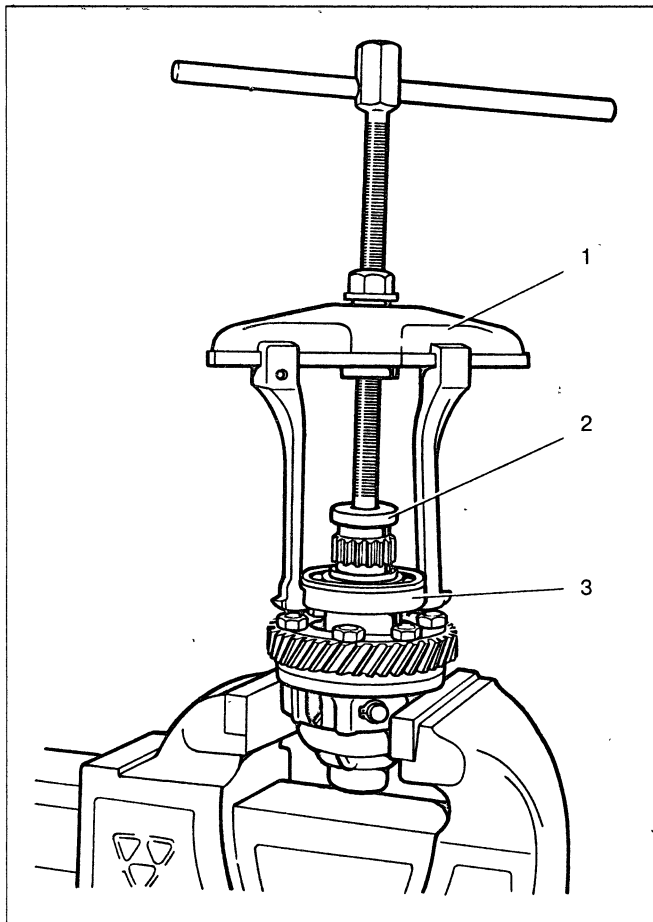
Спрессовка подшипника с корпуса дифференциала: 1 – съемник А.40005/1/6; 2 – упор. 67.7853.9559; 3 – подшипник
